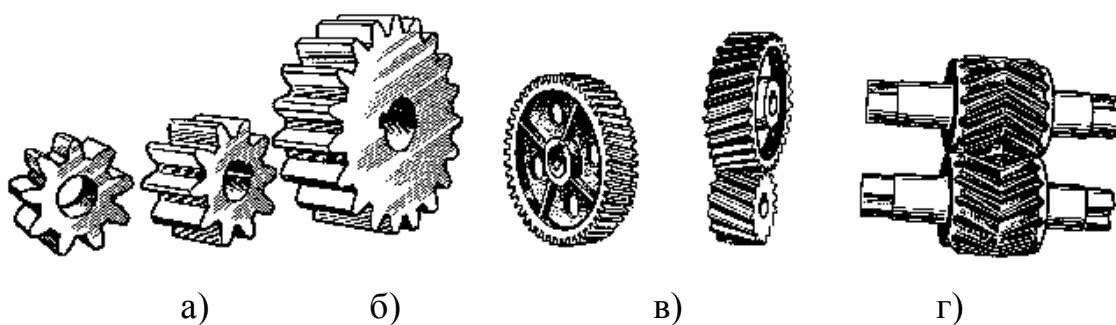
Виды зубчатых колес: а – сплошной диск; б – диск с ребром; в – косозубое; г – шевронное
